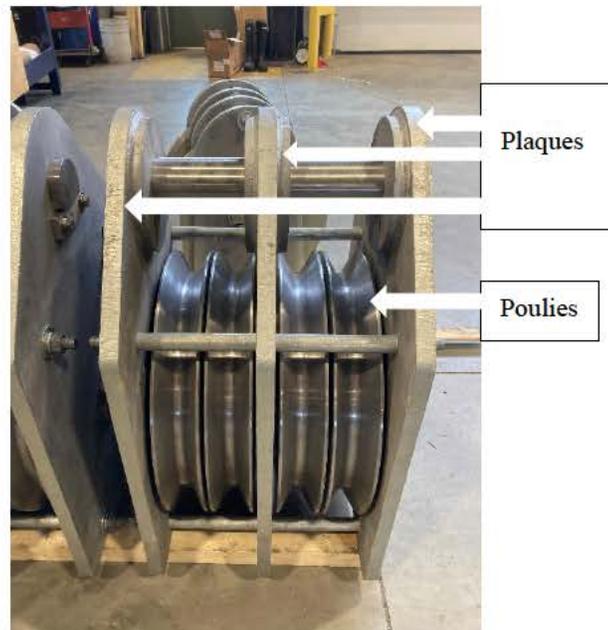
Moufle de levage inférieur assemblé (vue de face)
